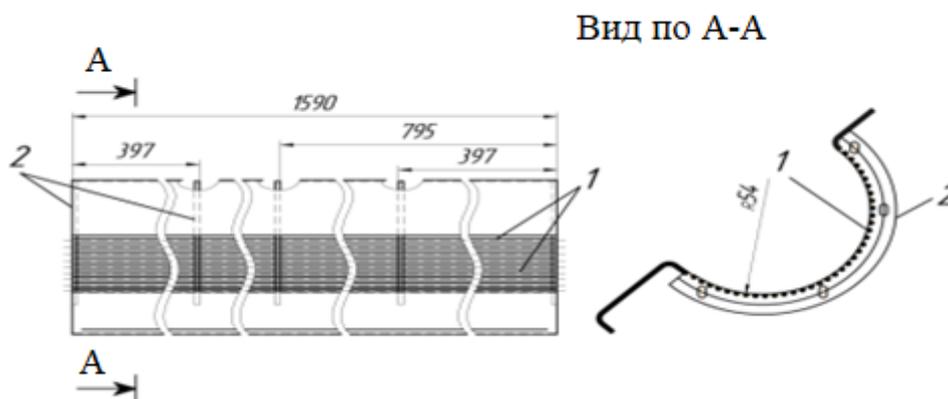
Сборочный чертеж промышленно-опытного образца усовершенствованной колосниковой решетки
